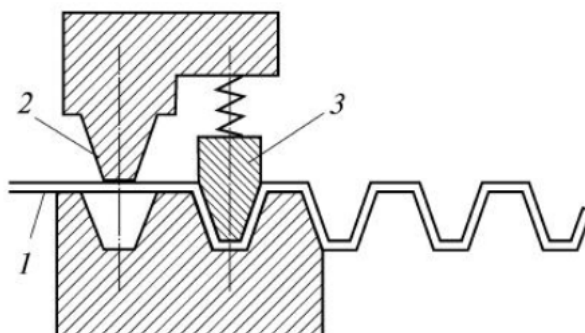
Штамп для получения гофрированных проставок: 1 – заготовка (лента); 2 – гибочный пуансон; 3- прижимной пуансон
